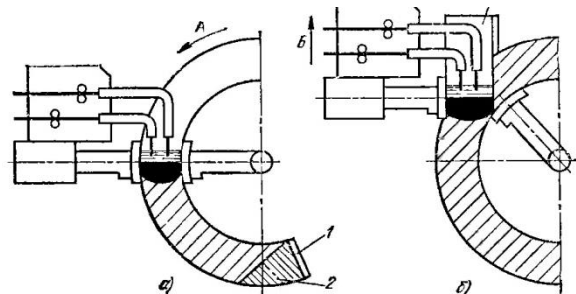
Электрошлаковая сварка кольцевого шва: а - вырезка дефектов в начале сварки; б - замыкание шва; стрелки:
